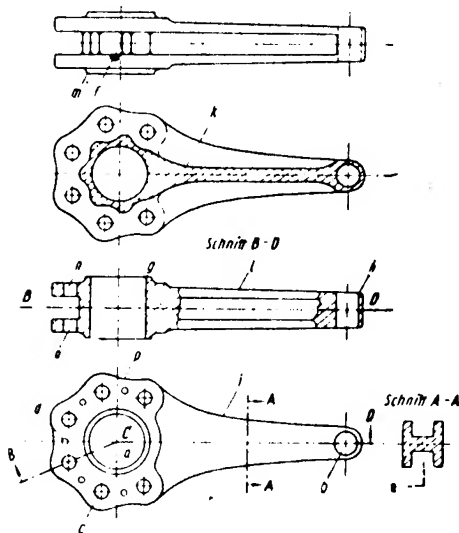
Hauptpleuelstange des Kolbenflugmotors ASch 82 T
